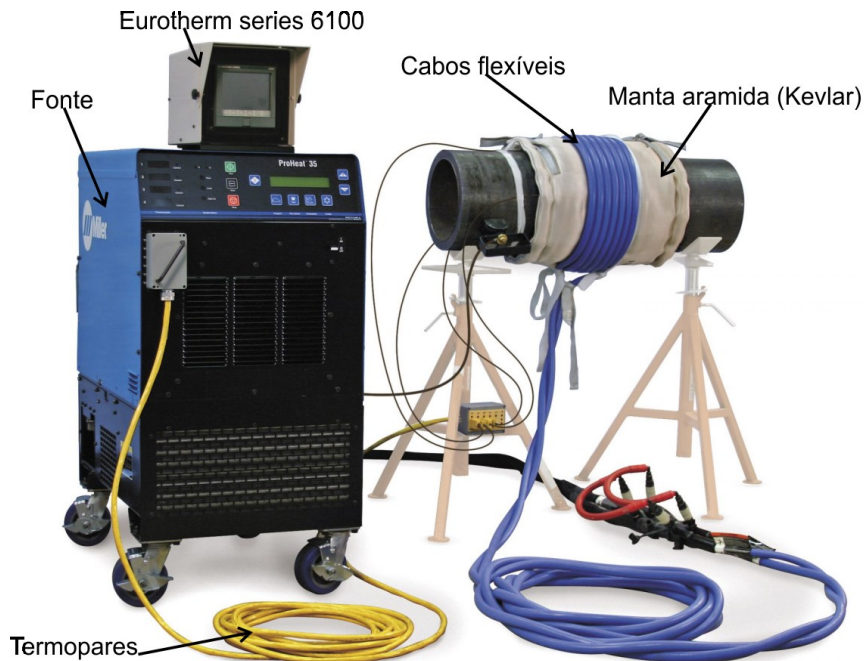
Sistema de aquecimento por indução Miller. Adaptado de Miller [122].
